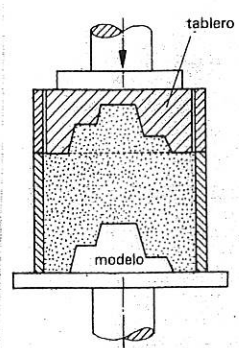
Empleo de tablero perfido en el moldeado por presión.
